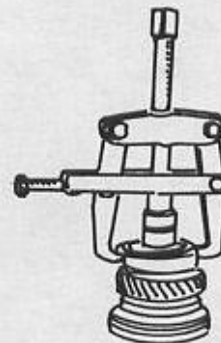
WYMONTOWANIE PIERŚCIENI ZABEZPIELAJĄCYCH TULEJĘ PROWADZĄCĄ
